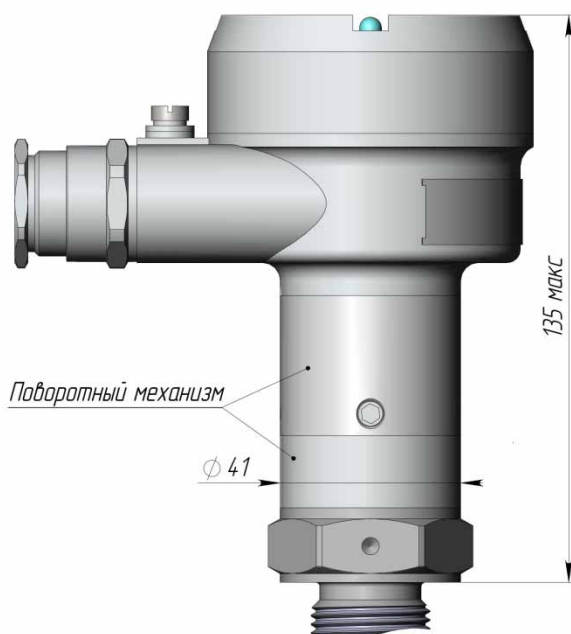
Габаритные размеры перехода на 160°C (100°C) с поворотным механизмом
